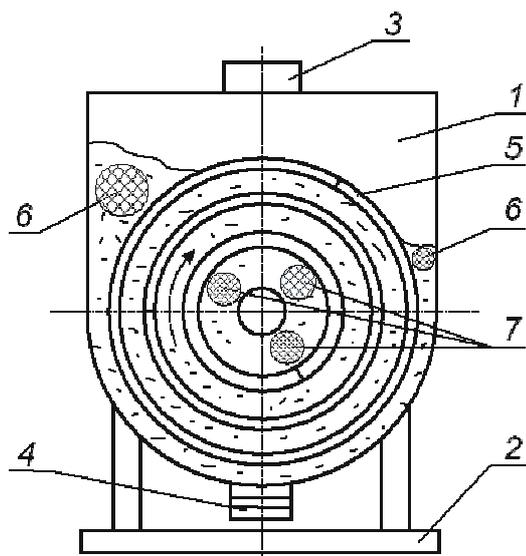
Общий вид смесителя: 1 - чашеобразный бункер; 2 - рама; 3 - загрузочный патрубок; 4 - выгрузной патрубок; 5 - комбинированный шнек; 6 - застойные зоны в верхней части бункера; 7 - застойные зоны в области вала шнека смесителя
